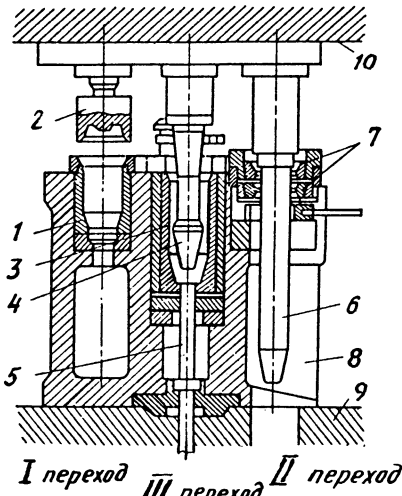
Штамп для изготовления крупных поковок типа стаканов:
